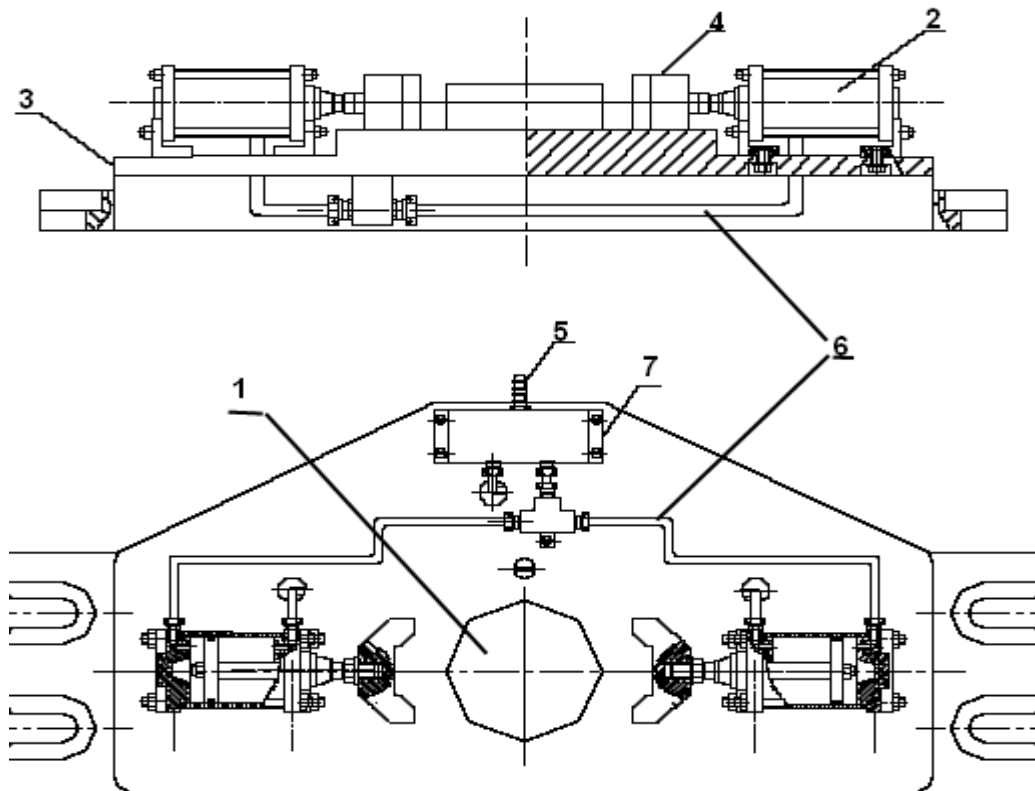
Конструкція автоматизованого верстатного пристрою
